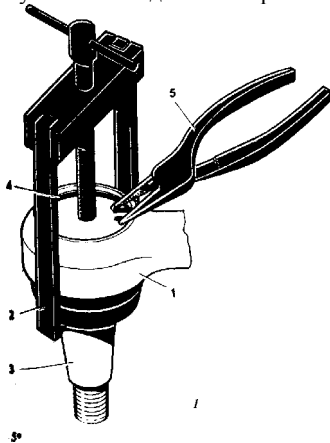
Извлечение запорного кольца шарового пальца 1 - рулевая тяга, 2 - съемник, 3 - шаровой палец, 4 — запорное кольцо, 5 — круглогубцы надавить на заглушку.
